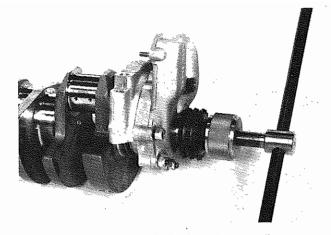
Smontare II pignone distribuzione e la pompa clio Disassemble distributor pinion and cil pump
